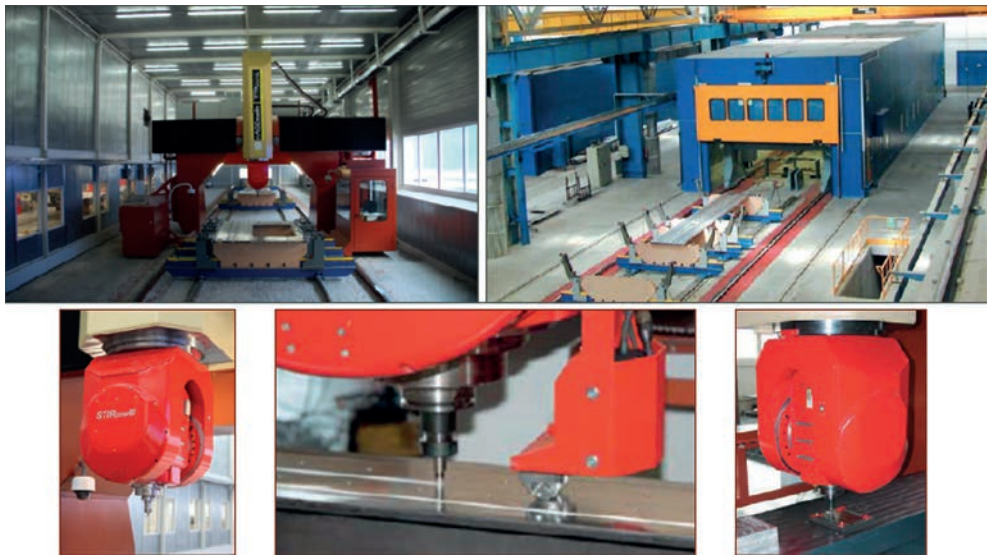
Приклад обладнання HAGEMATIC 305 FSW з фрезерно-зварювальною голівкою STIRPOWER 300 для високошвидкісного фрезерування та ЗТП для з’єднання габаритних плоских секцій
